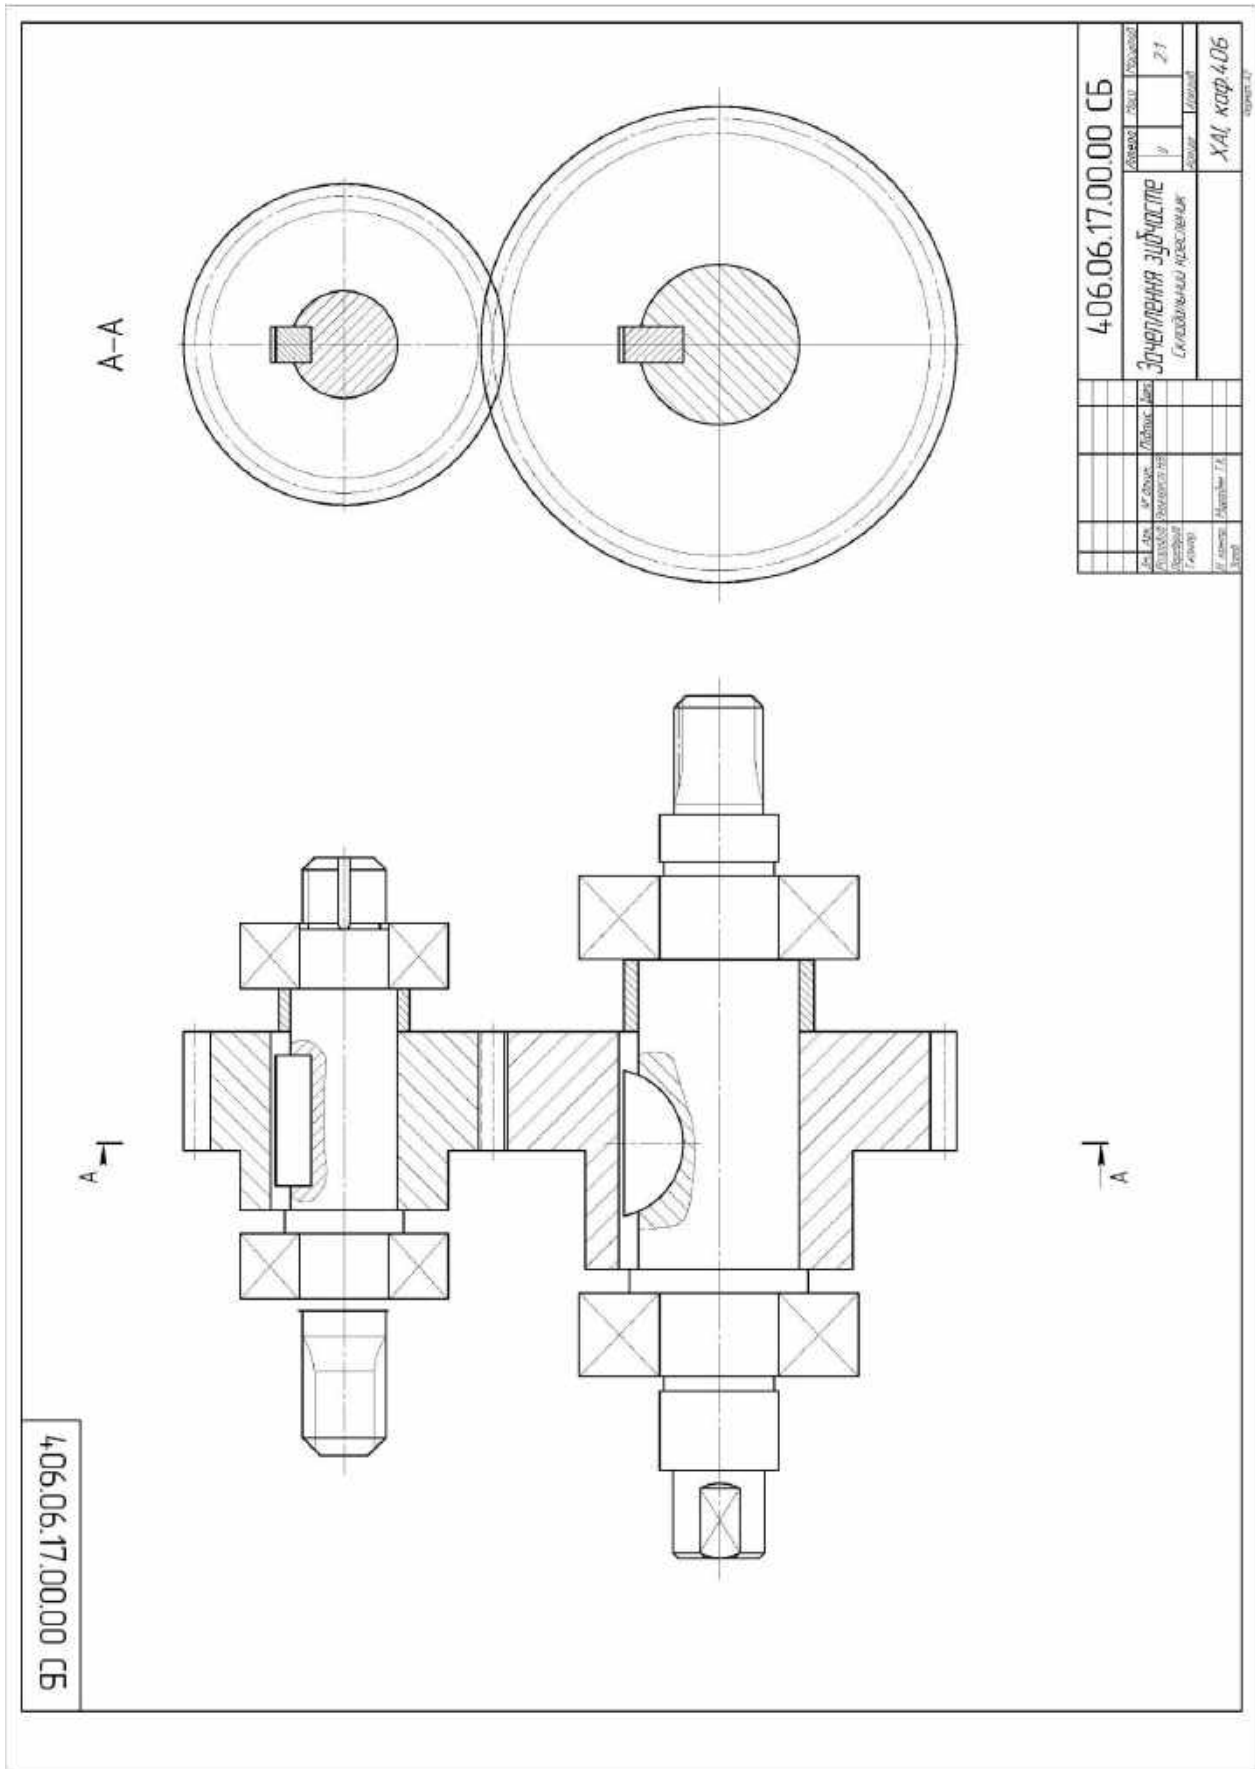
Четвертий етап виконання складального креслення зубчастого зачеплення з підшипниками
